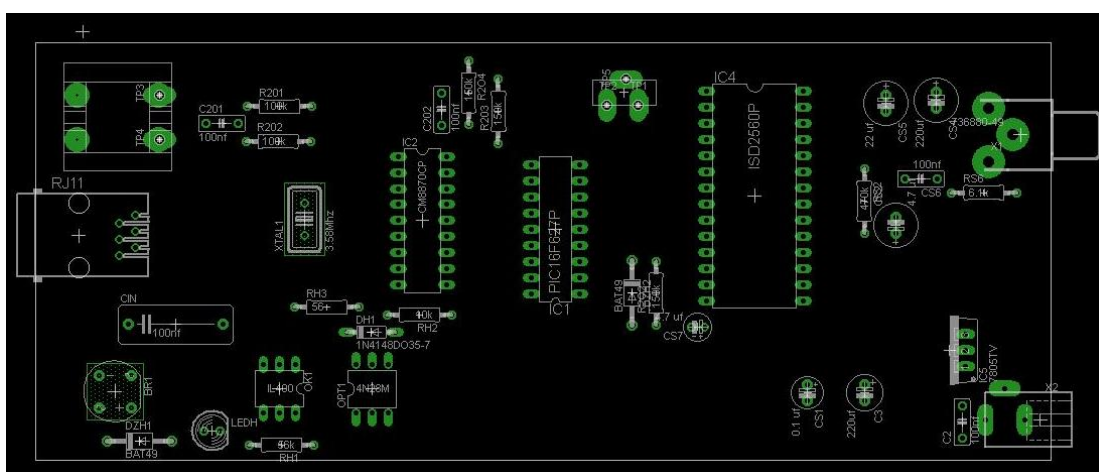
Diseño de la placa de circuito impreso, lado componentes. (No está a tamaño real)
